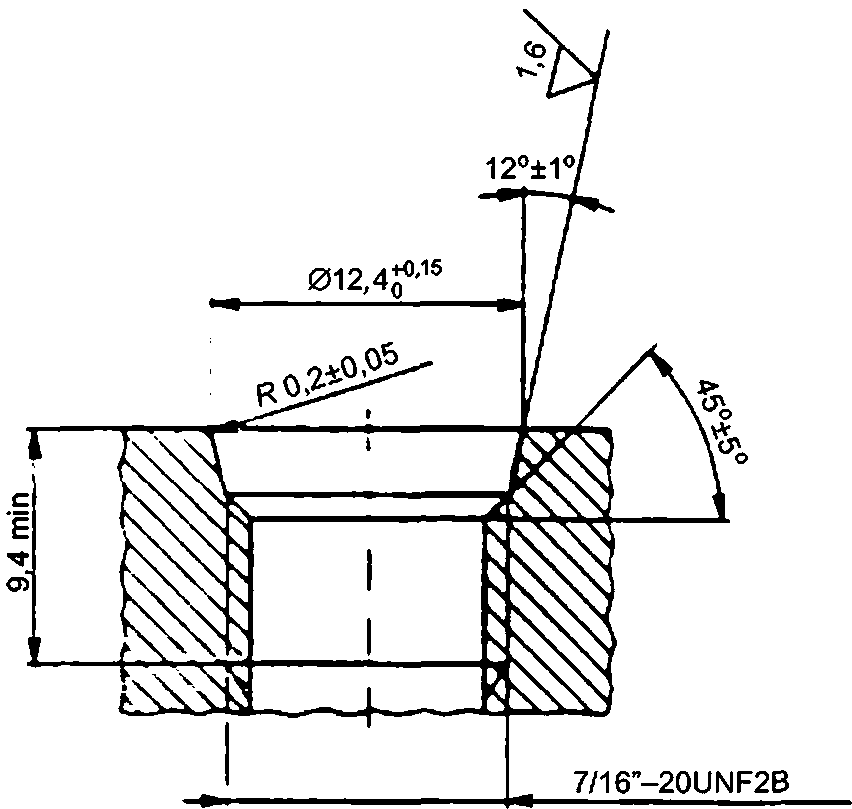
Внутрішнє з'єднання для гвинтової втулки 7/16-20
